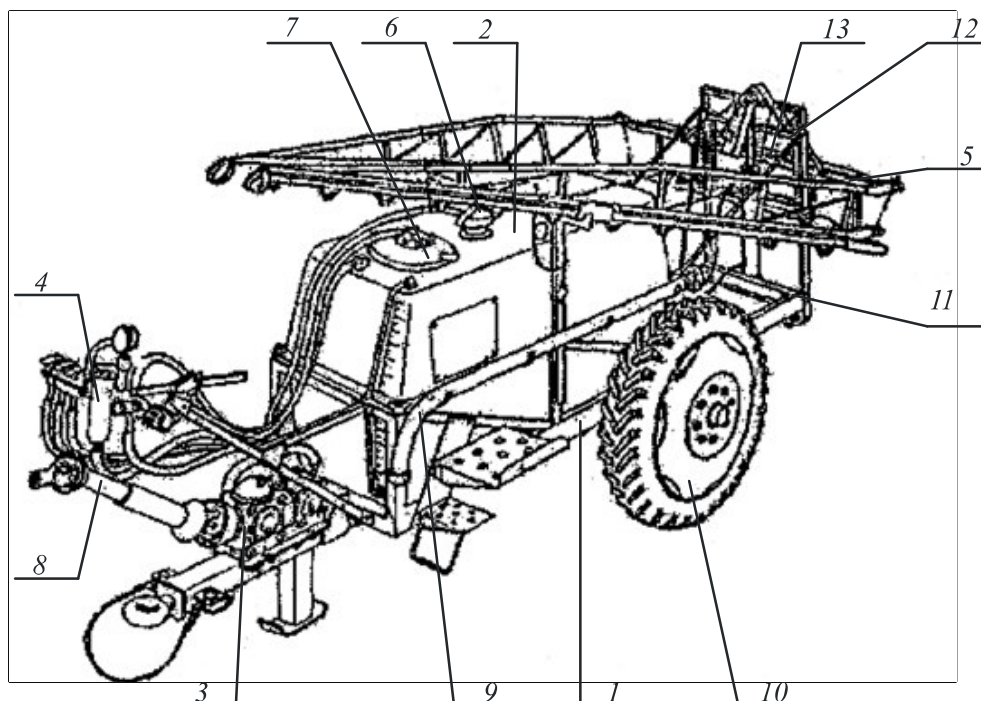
Опрыскиватель ОТМ 2-3: 1 – рама; 2 – бак (резервуар) для рабочей жидкости; 3 – насосный агрегат; 4 – регулятор давления в сборе с распределителем; 5 – штанга; 6 – всасывающая коммуникация с фильтром; 7 – корзина смешивания; 8 – карданная передача; 9 – рукав заправочный; 10 – колеса; 11 – рамка; 12 – ползун; 13 – гидроцилиндр
